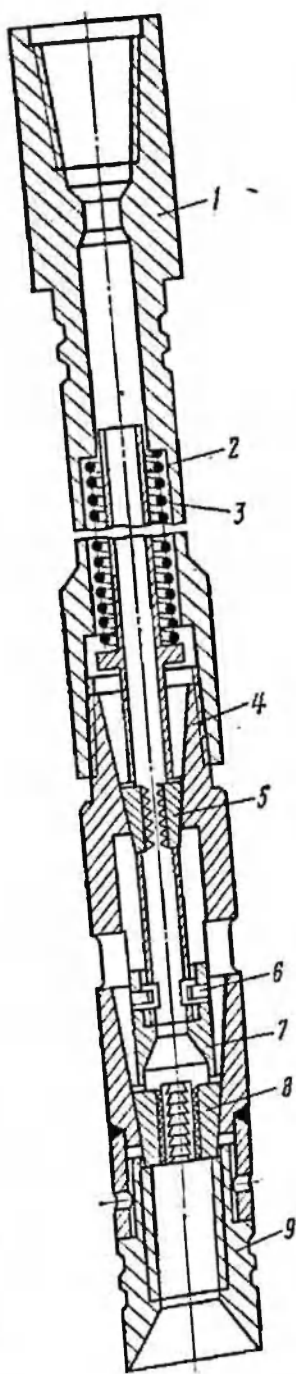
Комбинированный ловитель штанг и труб ЛКШ-114
